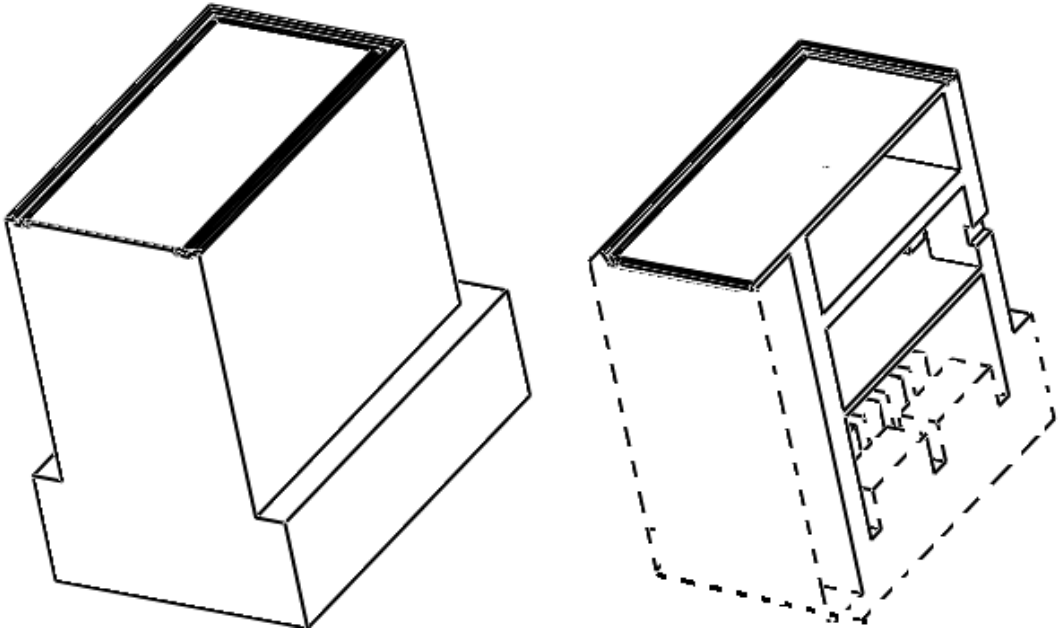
Elementos estructurales modelados con elemento finito Shell Thin.
